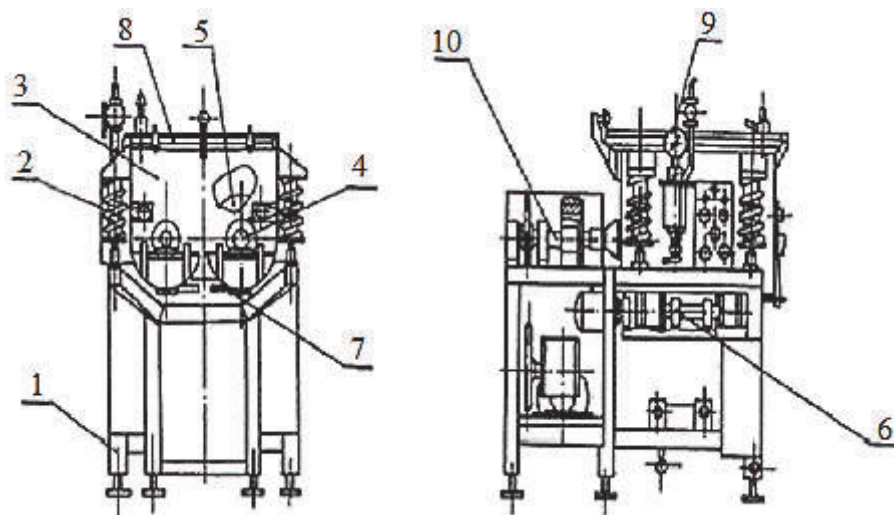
Фаршемешалка шнековая: 1 – рама; 2 – виброопоры; 3 – загрузочная емкость; 4 – два горизонтальных вала; 5 – шнеки; 6 – дебалансный вибратор; 7 – выгрузочные люки с крышками; 8 – герметичная верхняя крышка; 9 – устройство для присоединения загрузочной емкости с вакуумной системой; 10 – привод
